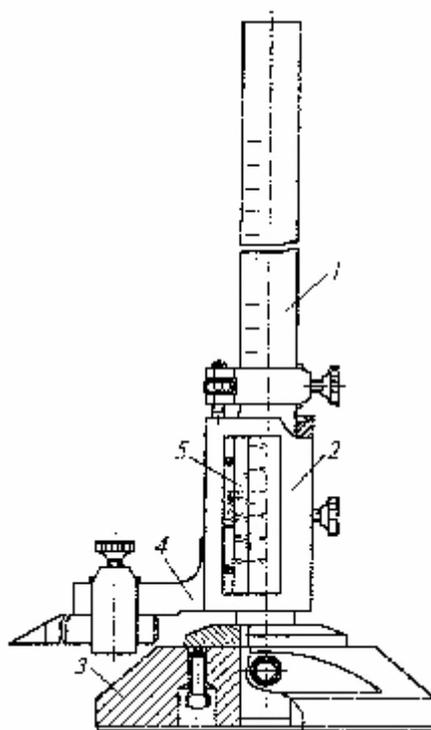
Штангенрейсмас: 1- штанга-линейка; 2- рамка; 3- основание; 4- державка; 5- нониус
